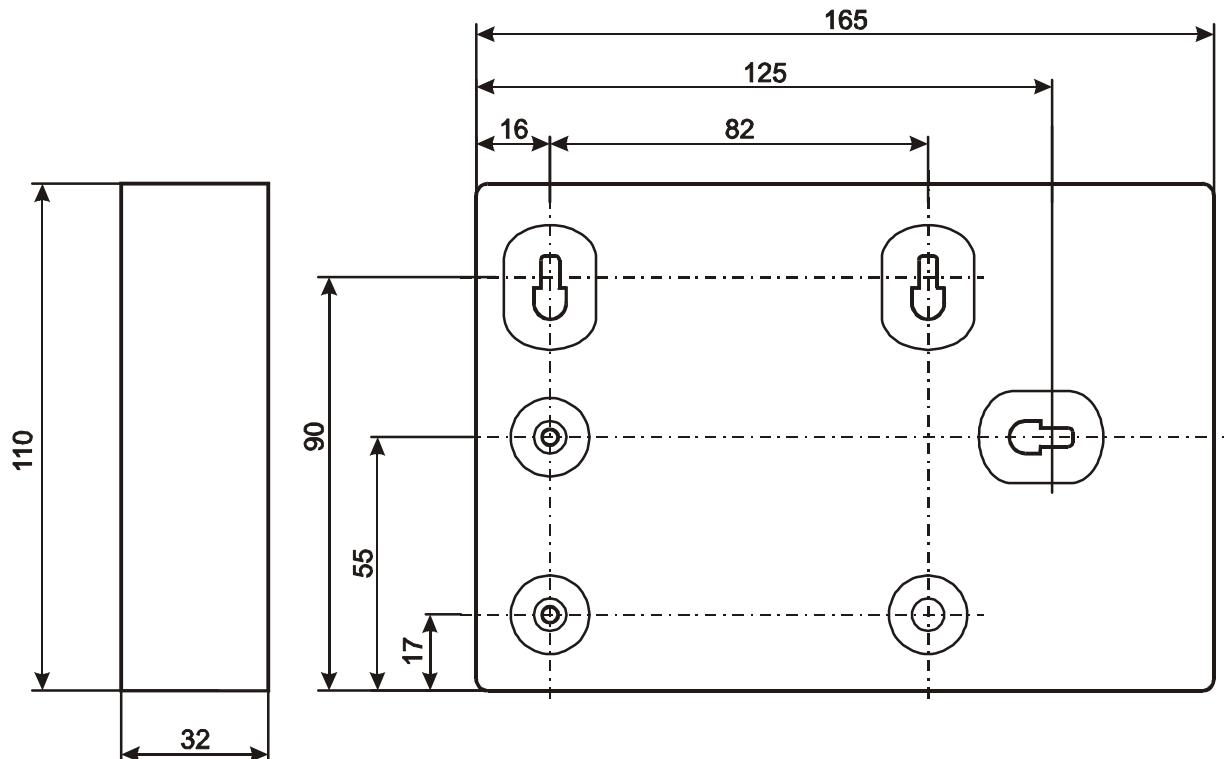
Внешний вид, габаритные и присоединительные размеры (исполнение IP20)
